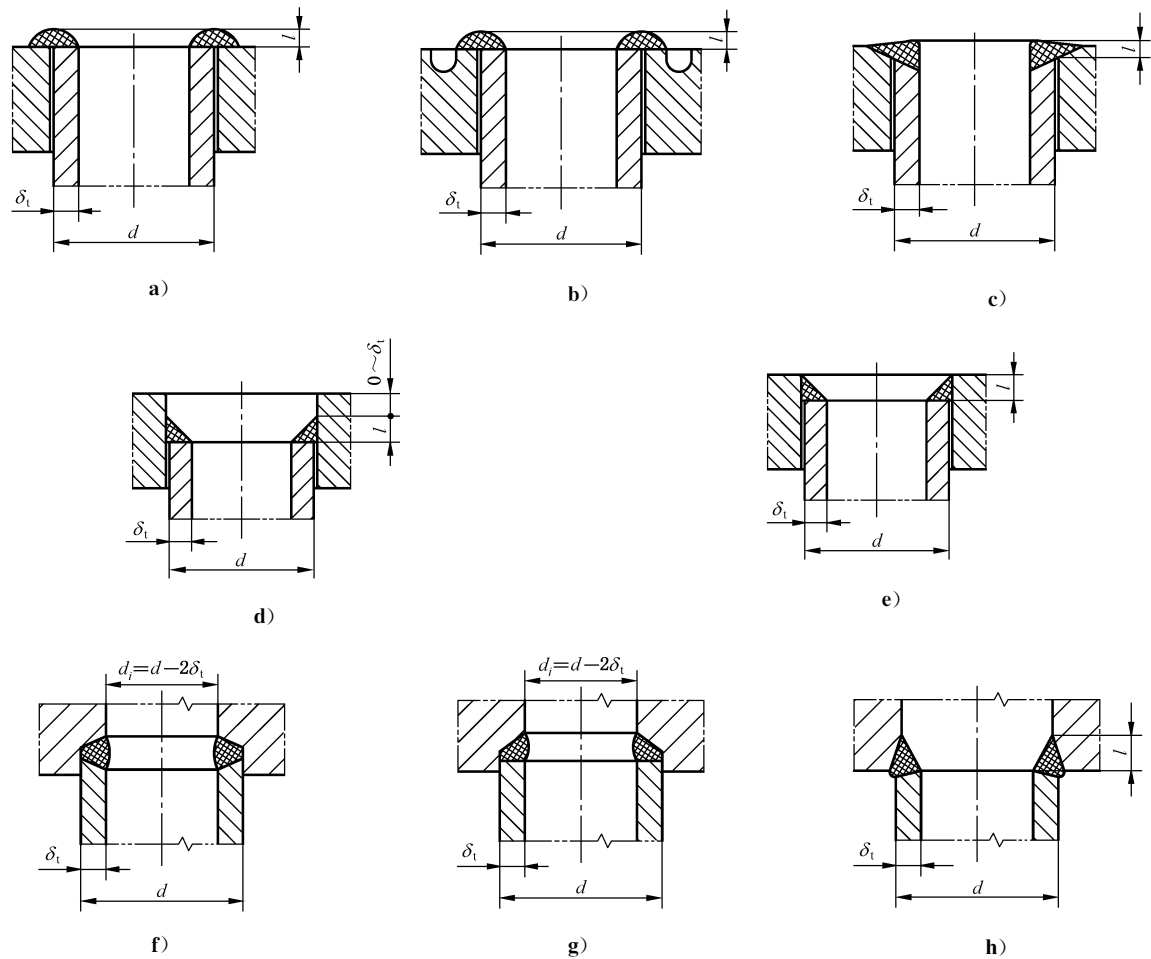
换热管与管板焊接接头的焊缝形式
